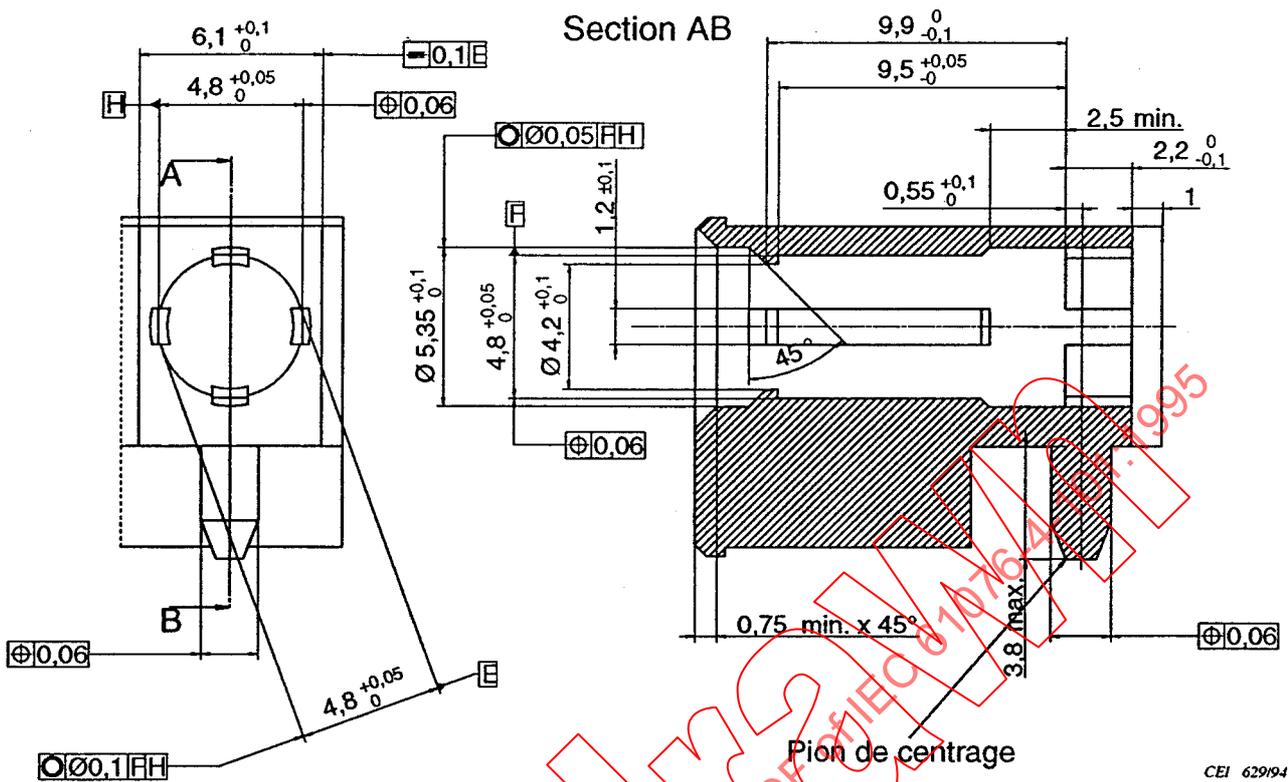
Dimensions des alvéoles de fiche pour contacts spéciaux
